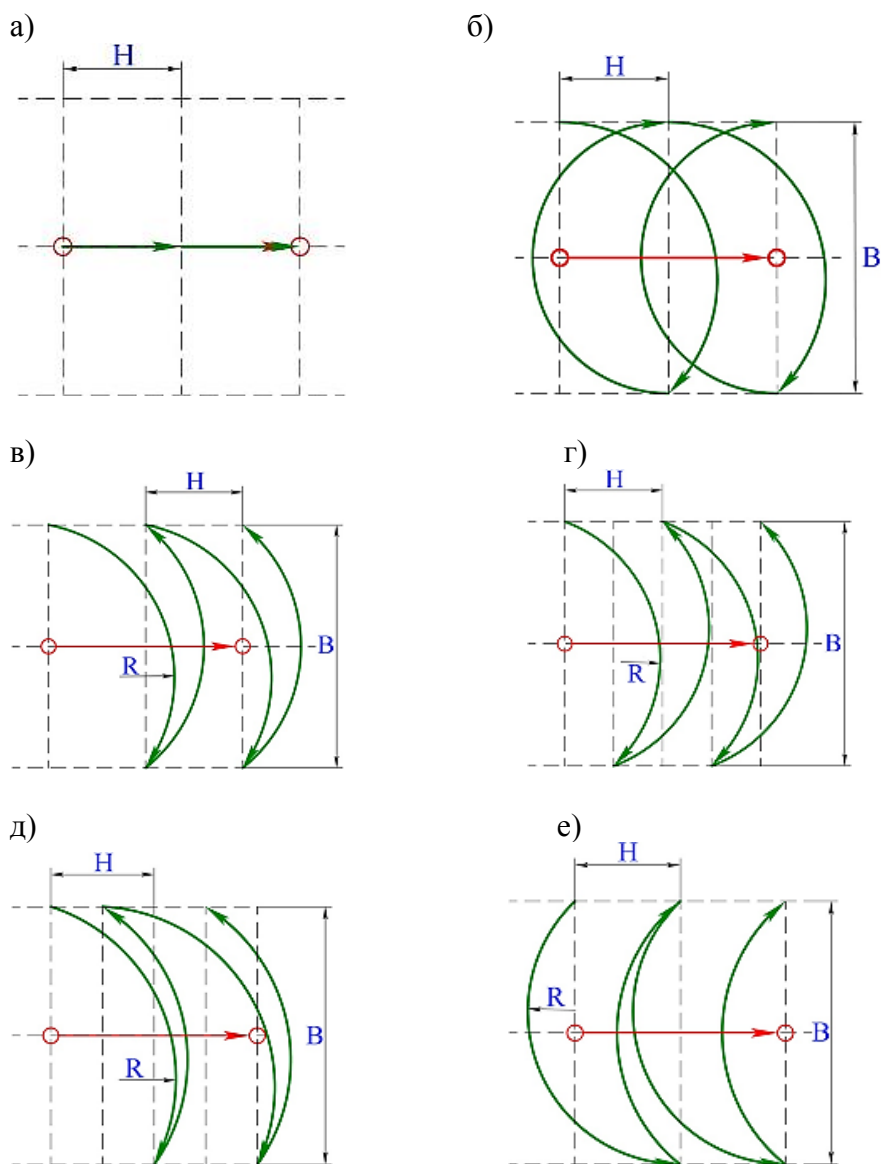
Типы траекторий перемещения сварочной горелки:
